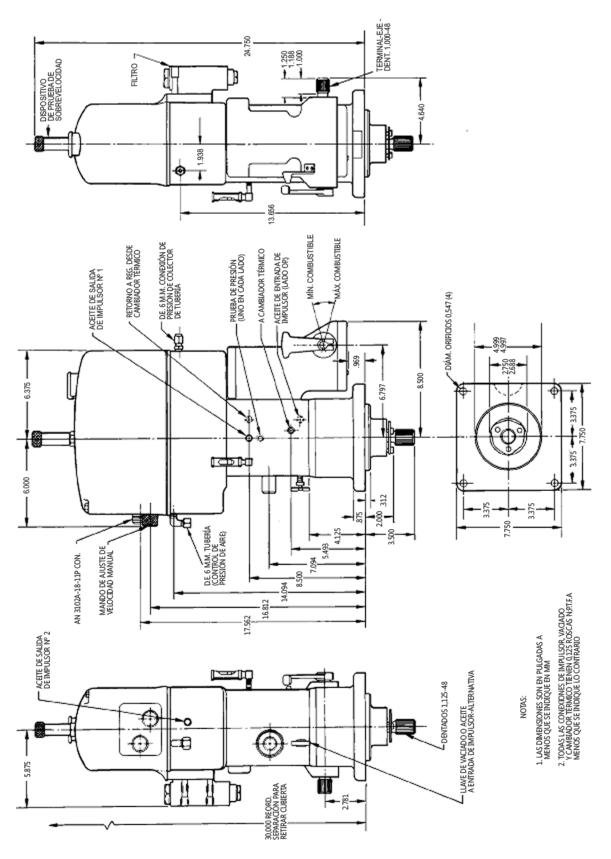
Plano esquemático de PGA con salida rotatoria de 58 pies-libra y base UG-40 (No usar para construcción).
